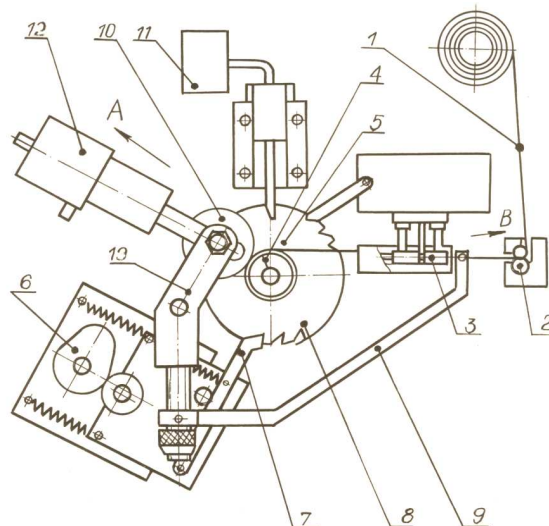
Схема устройства для намотки магнитопровода ротора
